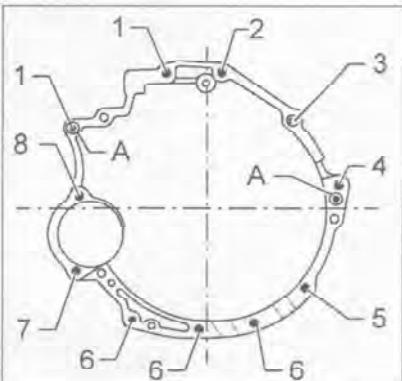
Последовательность затяжки болтов крепления коробки передач.
